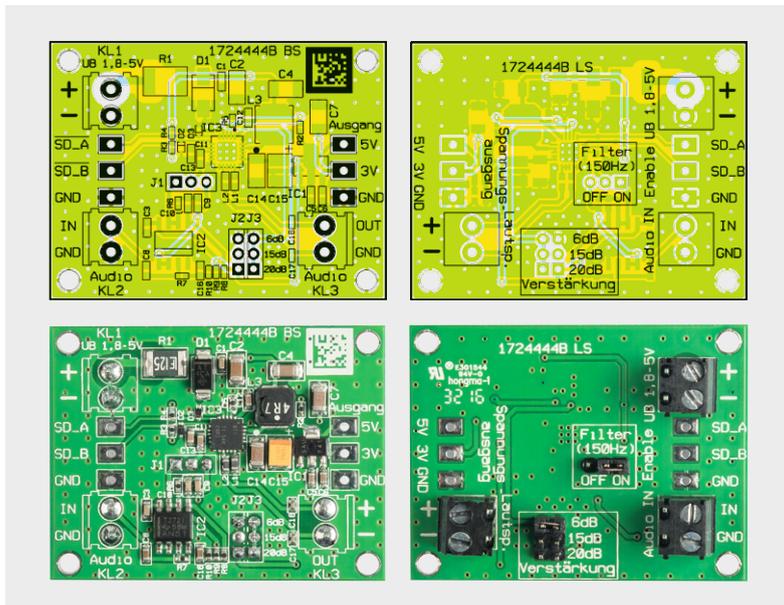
Die Platinenfotos des komplett bestückten DA2 mit den zugehörigen Bestückungsplänen. Hier sind die Schraubklemmen und Stiftleisten auf der Unterseite bestückt.
